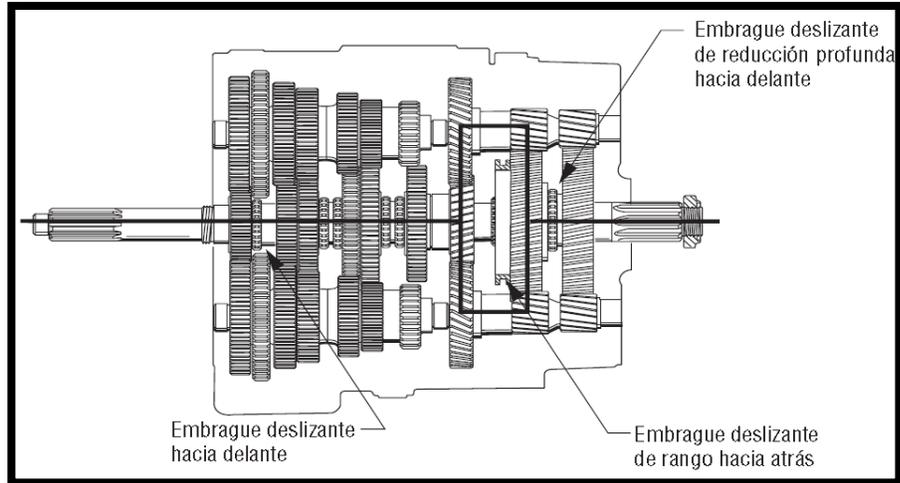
Engrane directo, transmisión tráiler: Fuente [34]
